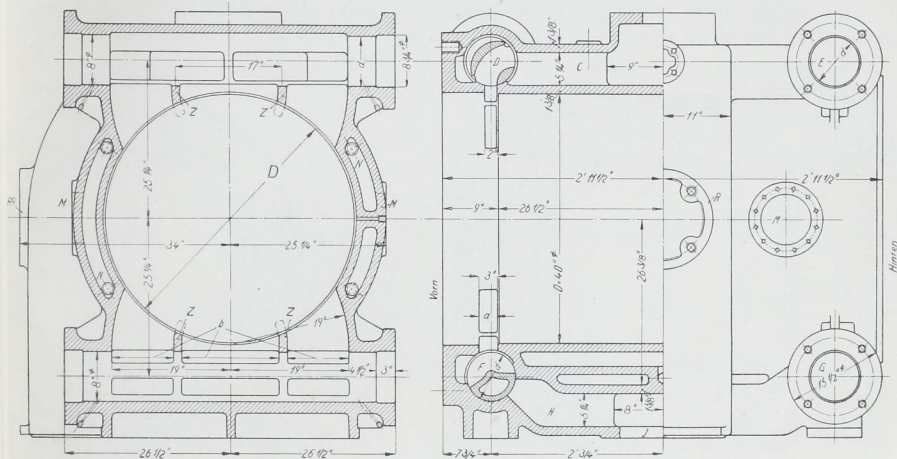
Zylinder mit Hahnsteuerung. Niederdruckzylinder der East-Jersey Wasserwerkmaschinen. Entwurf von Riedler und Stumpf. M. 1:25.
